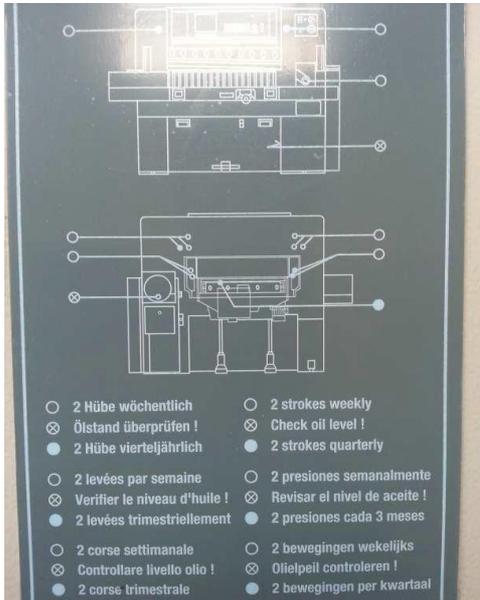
Instruções de lubrificação em idioma estrangeiro
